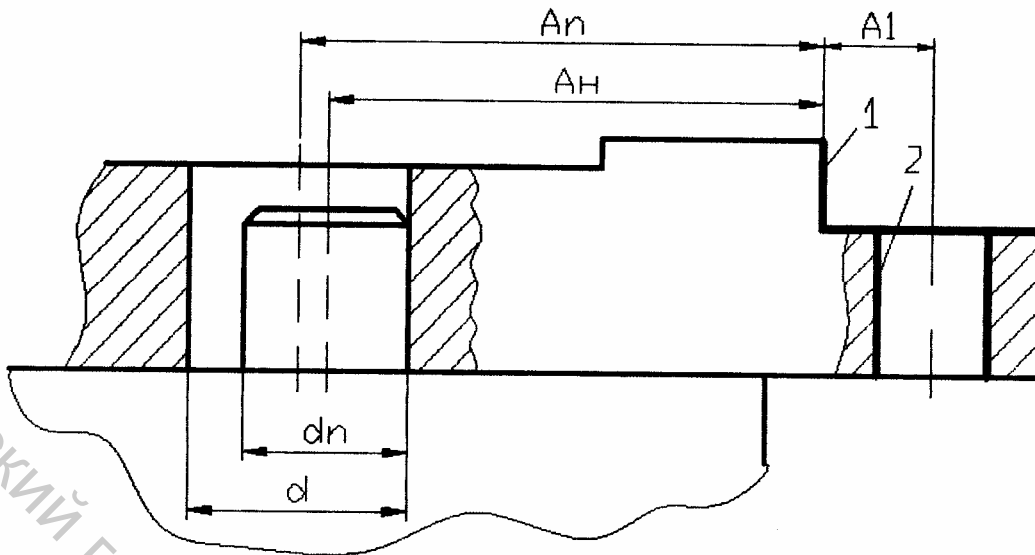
Установка заготовки по отверстию на цилиндрический палец
